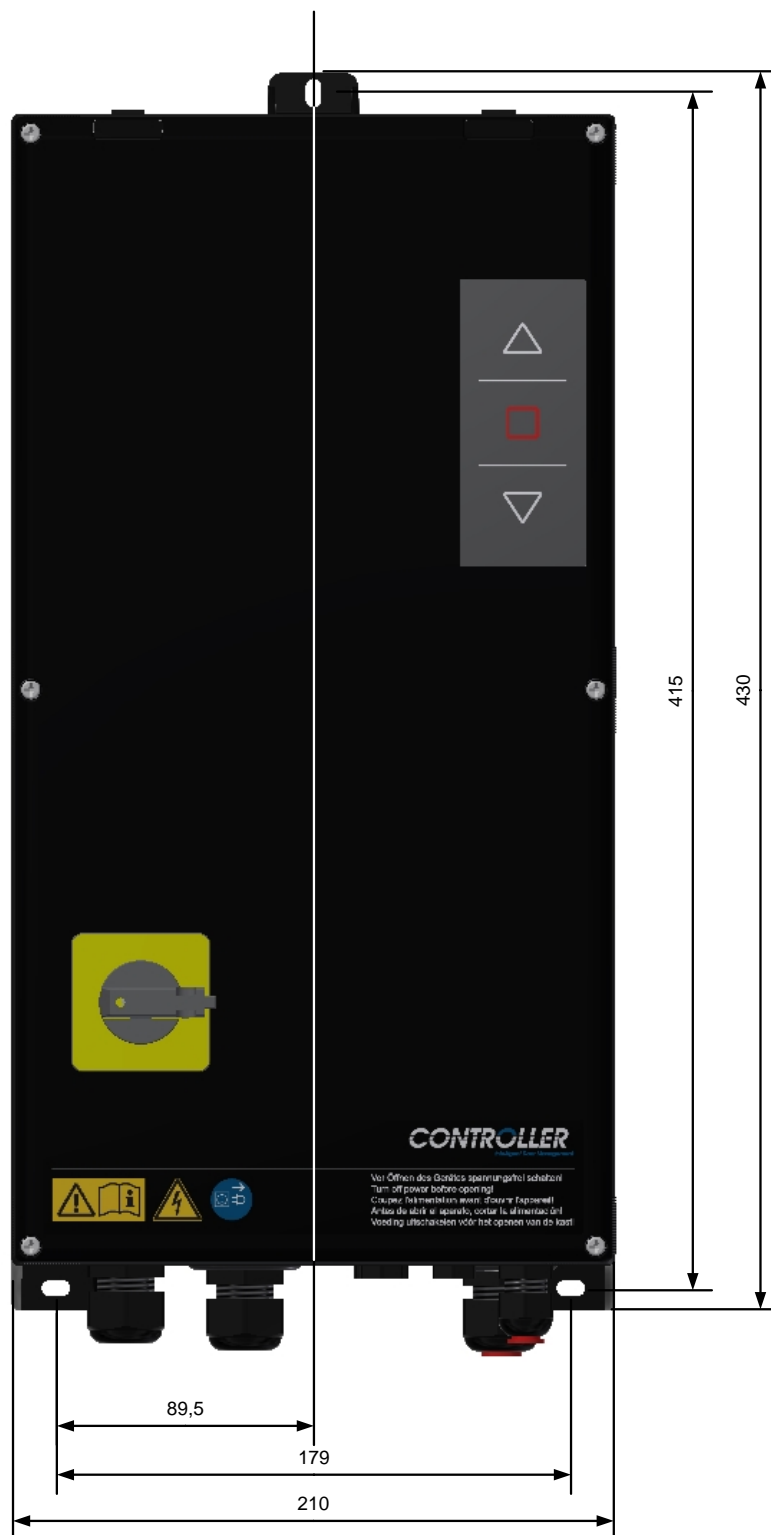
Dimensions et plan de perçage boîtier en plastique FUxF-xH
